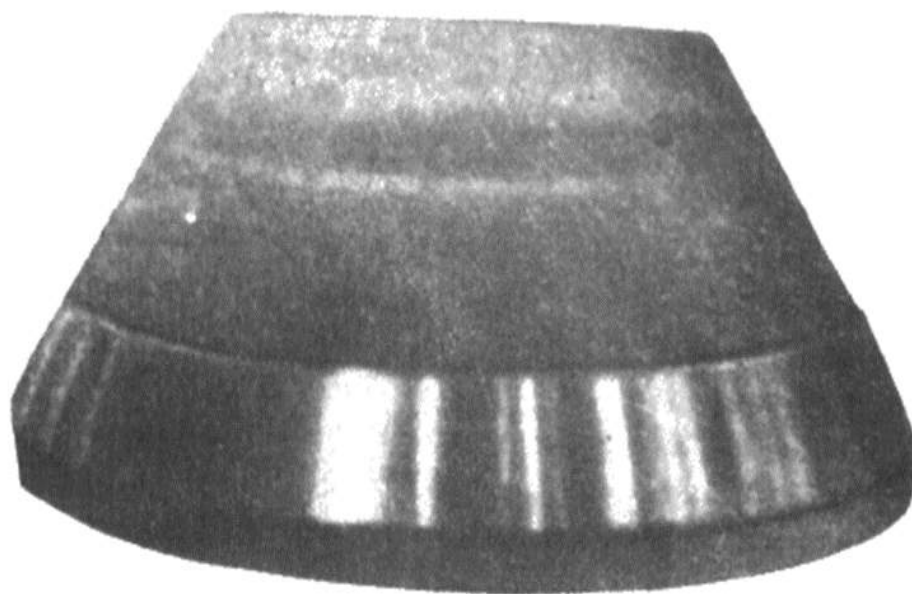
Малий конус, наплавлений композиційним сплавом після пічного наплавлення
